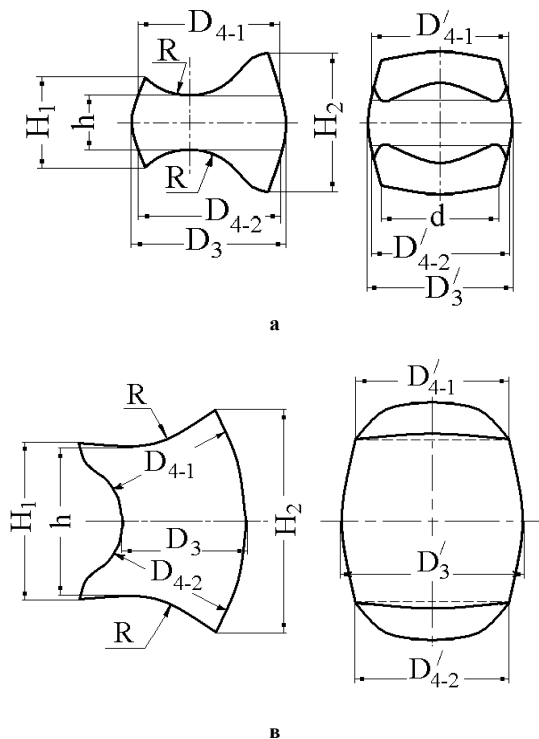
Схема обмера и образцы после эксцентричной осадки выпуклыми бойками с радиусом R :
